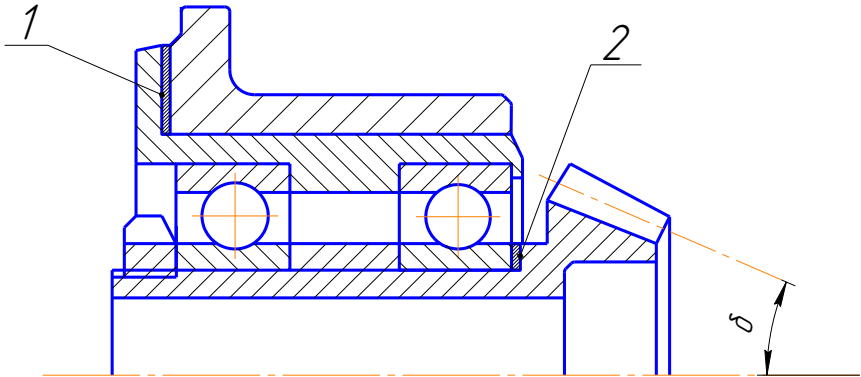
Примеры расположения компенсаторов для обеспечения бокового зазора в зацеплении конических зубчатых колес
